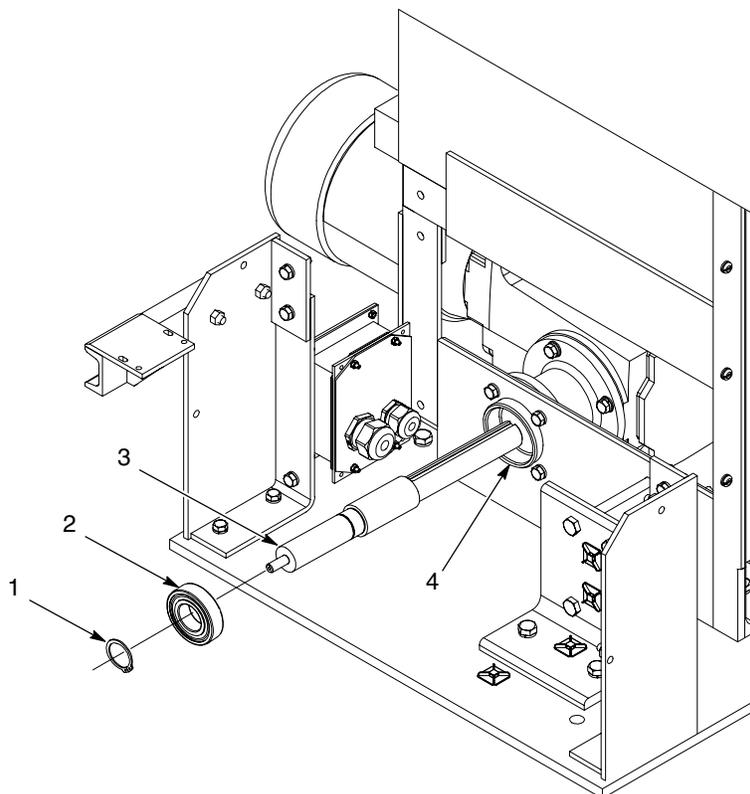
Remplacement du palier ou de l'arbre du motoréducteur
